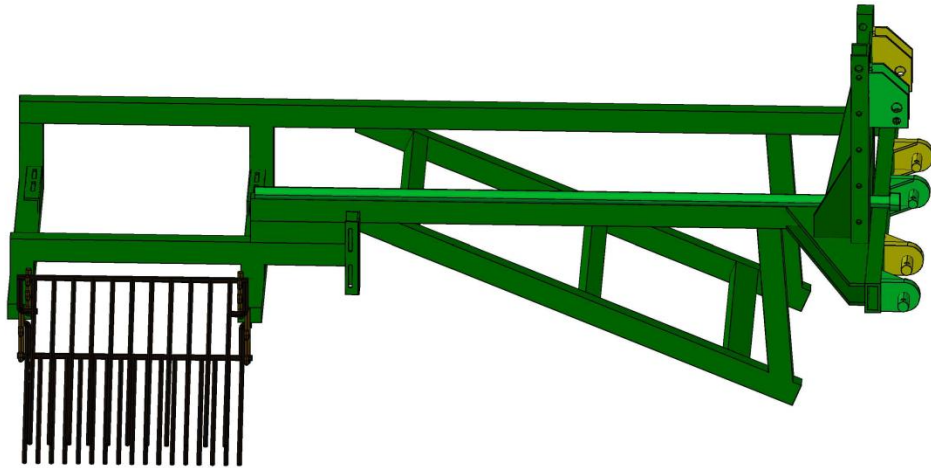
Rejillas seleccionadoras montada al chasis de la máquina arrancadora de papa
